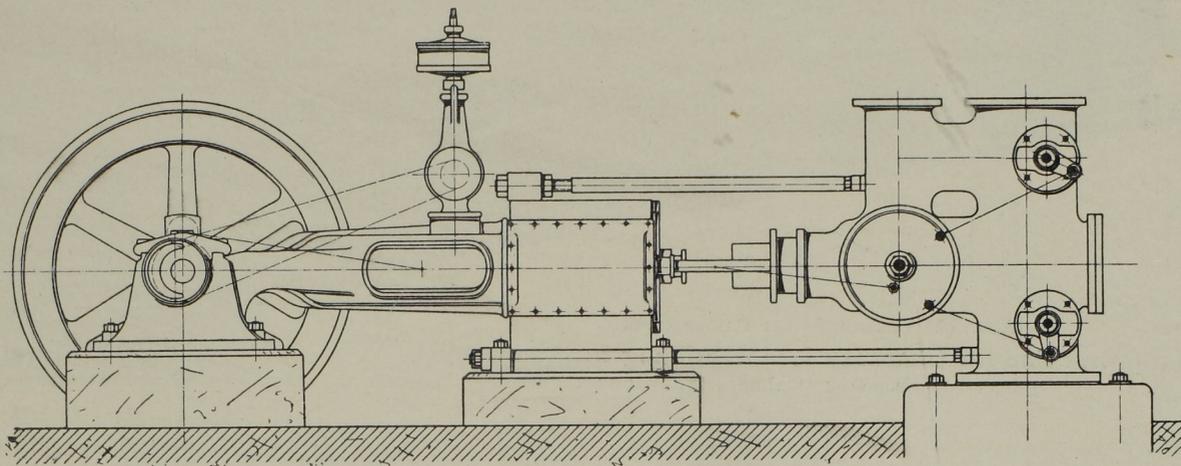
Seitenansicht der Pumpmaschine. Massst. 1 : 32.
